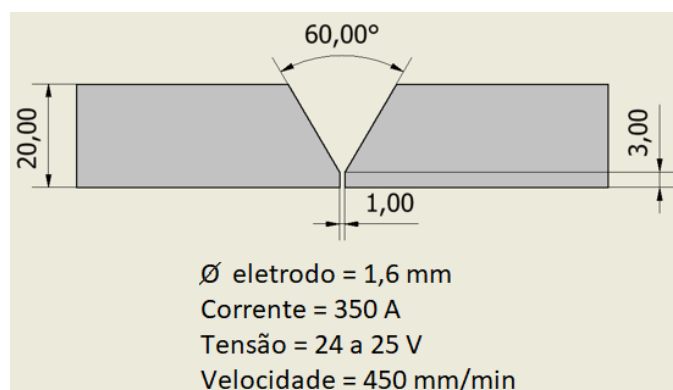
Especificação de geometria para o chanfro em V e parâmetros de soldagem (dimensões em milímetros).
